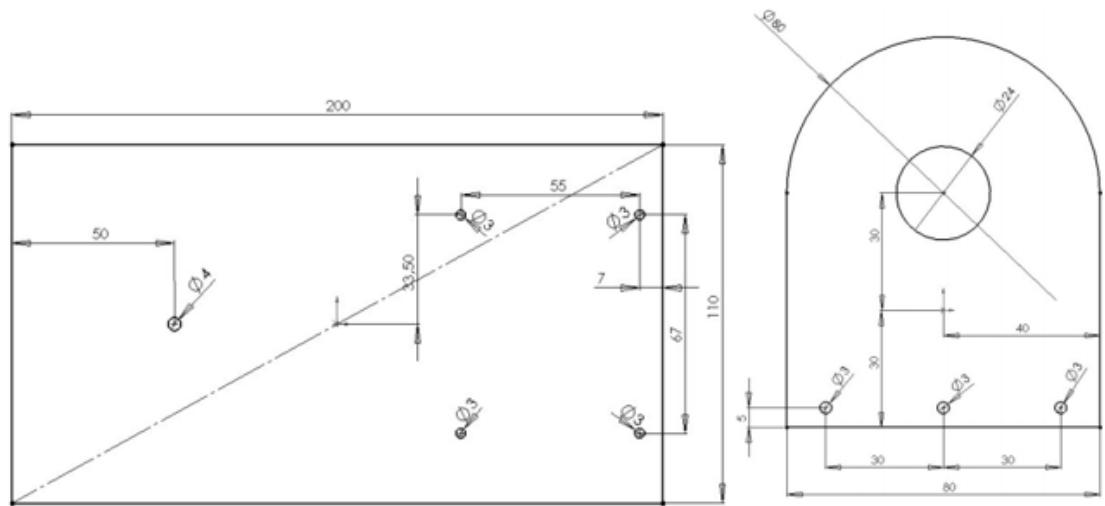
Vistas de lateral y de planta de pieza de brazo robótico.
